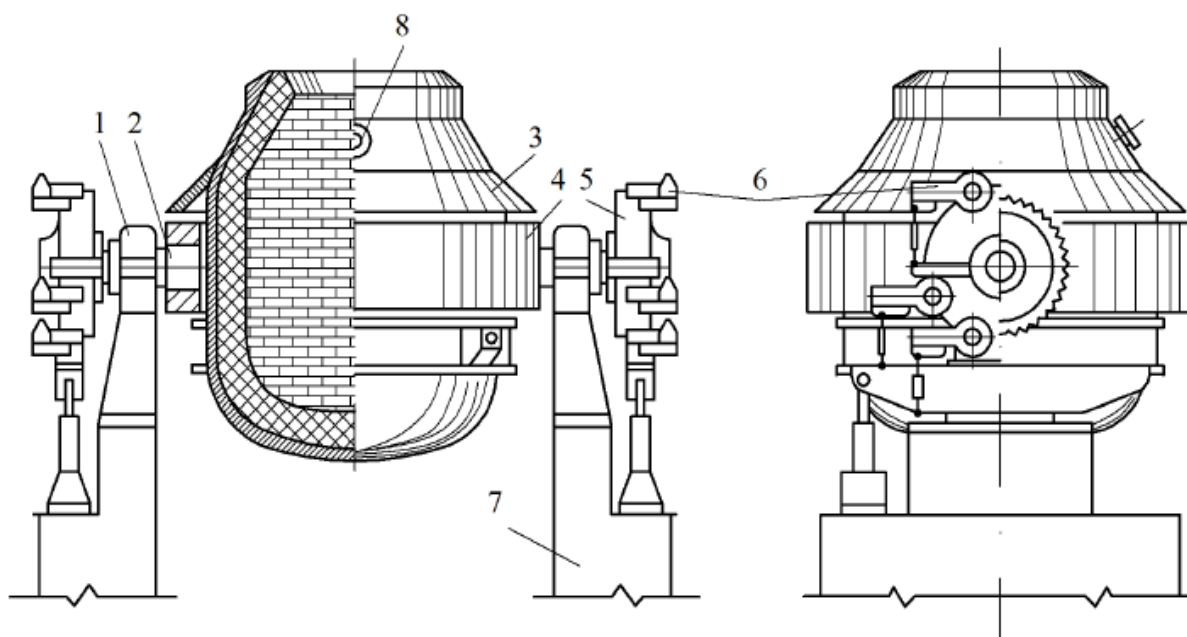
Кислородный конвертер: 1 - опорный подшипник; 2 - цапфа; 3 - кожух; 4 - опорное кольцо; 5 - ведомое колесо; 6 - электродвигатель; 7 - опорная станина; 8 –летка
